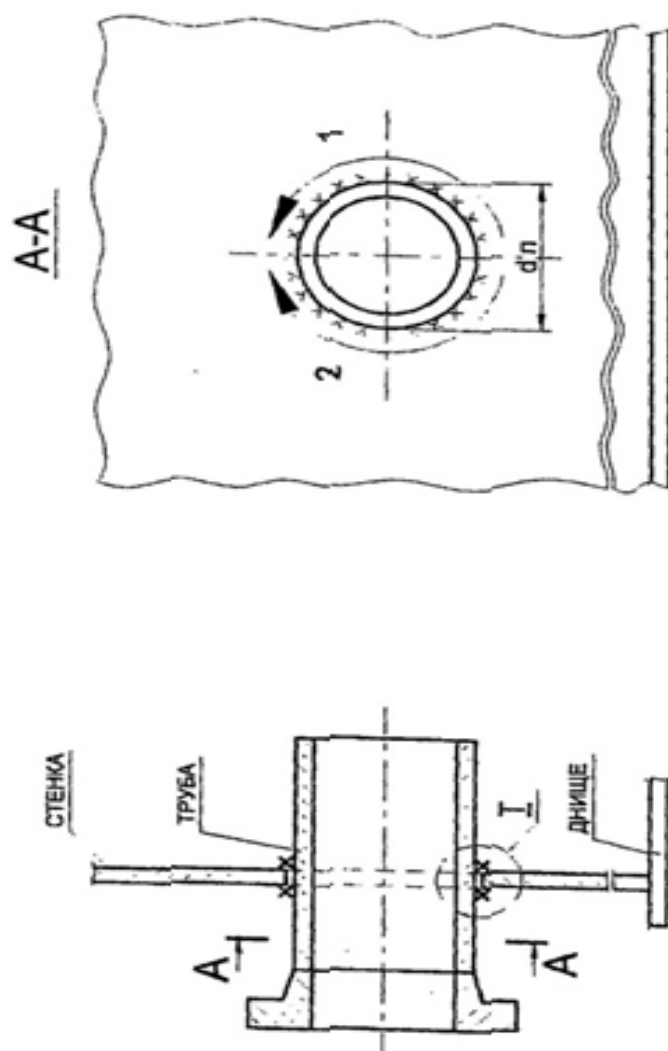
Схема сварки патрубков в стенке без усиливающего листа
